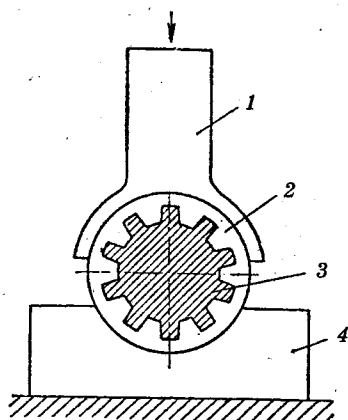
Осадка детали, имеющей шлицевое отверстие:
